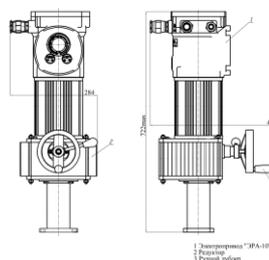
Чертеж электропривода РэмТЭК-02
